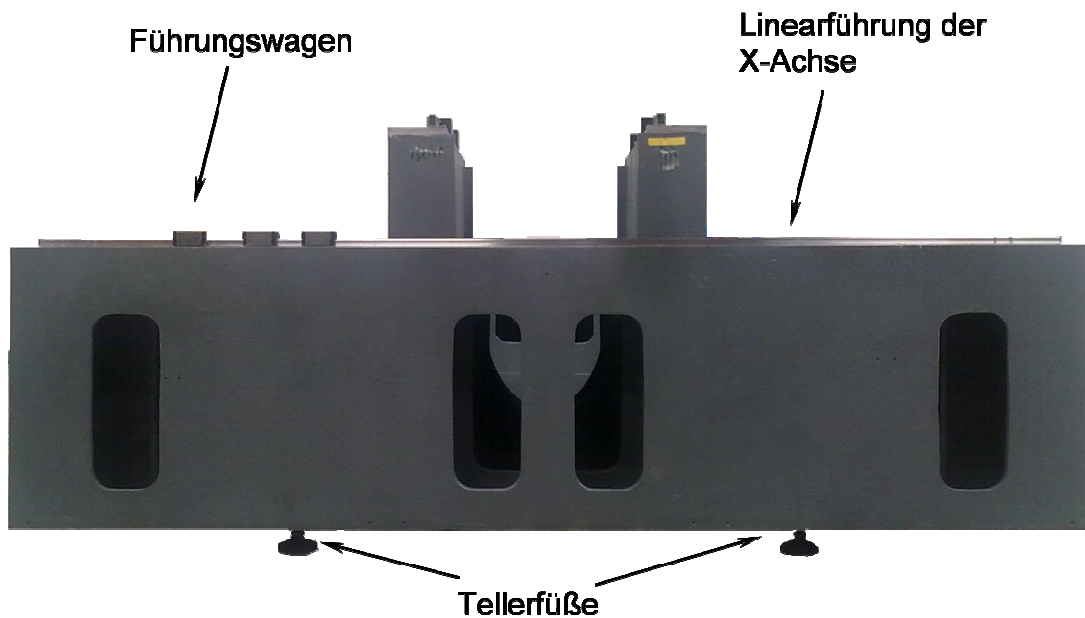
Maschinenbett mit fertig montierter Linearführung
